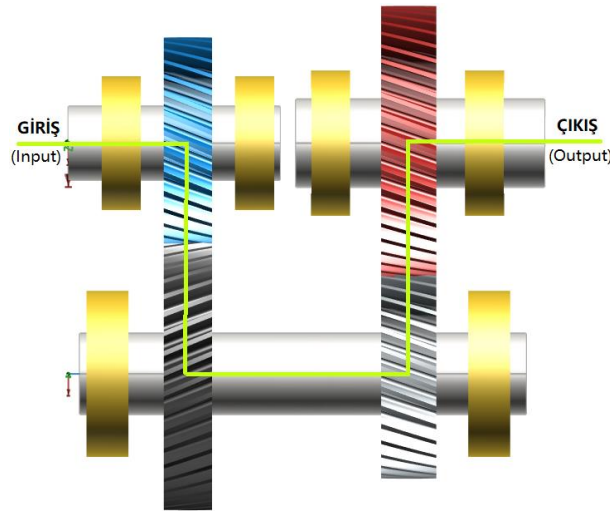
Vites kutusu boyutlarının sınır hacmi (The boundary volume of gearbox dimensions)
